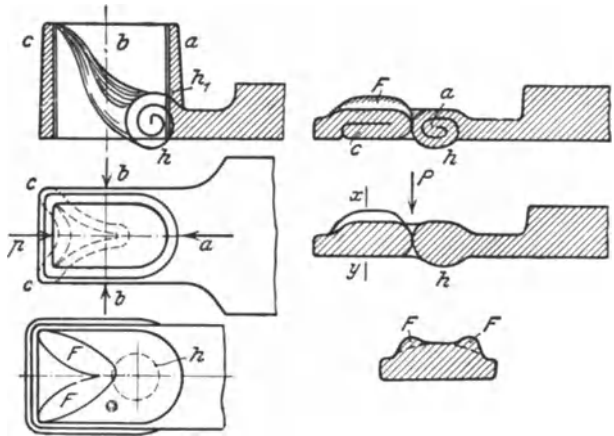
÷109. Faltungsvorgang bei einem abgerundeten Vierkantöhr.
